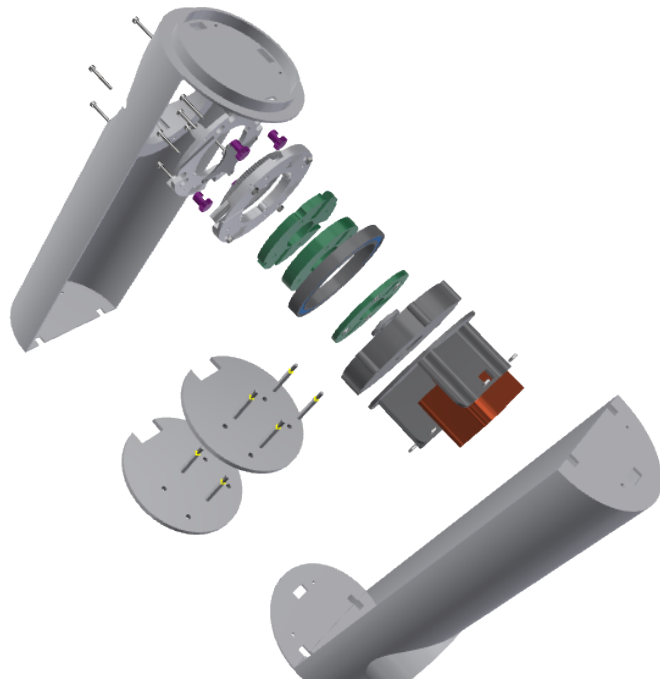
Explosionszeichnung eines Segmentes des modularen Yete-Roboterarms.
